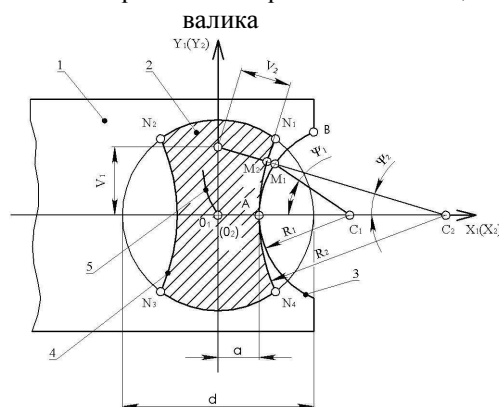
Исходное положение деталей шарнира качения: 1 – пластина; 2 – валик; 3 – выпуклая рабочая поверхность отверстия пластины; 4 – вогнутая рабочая поверхность валика; 5 – траектория движения центра валика
